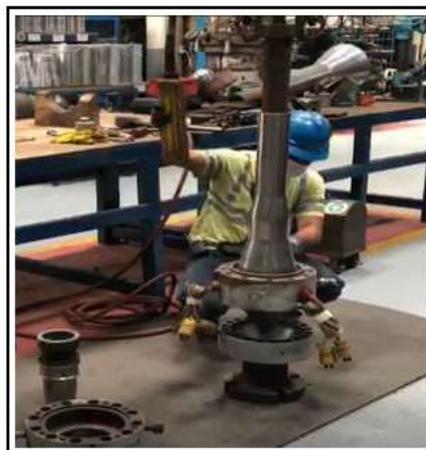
ACOPLA HEMBRA FINAL CON MACHO DEL MOLDE
